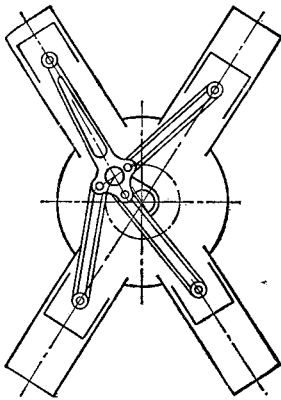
Схема двигателя с X-образным расположением цилиндров
